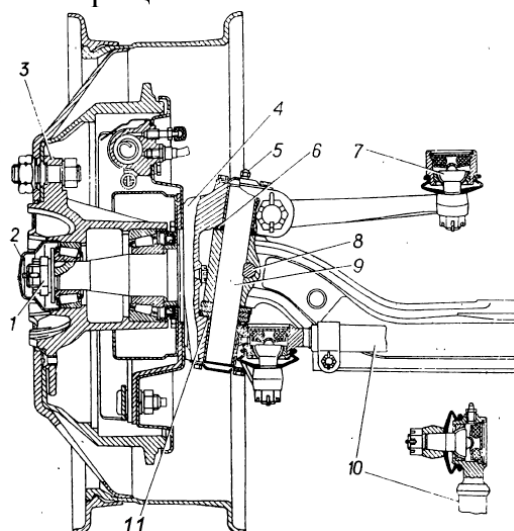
Передняя ось: 1 – гайка; 2 – колпак; 3 – ступица; 4 – поворотный кулак; 5 – клапан прокачки; 6 – регулировочные шайбы; 7 – палец, рулевой тяги; 8 – стопор; 9 – шкворень; 10 – рулевые тяги; 11 – уплотнительное кольцо
